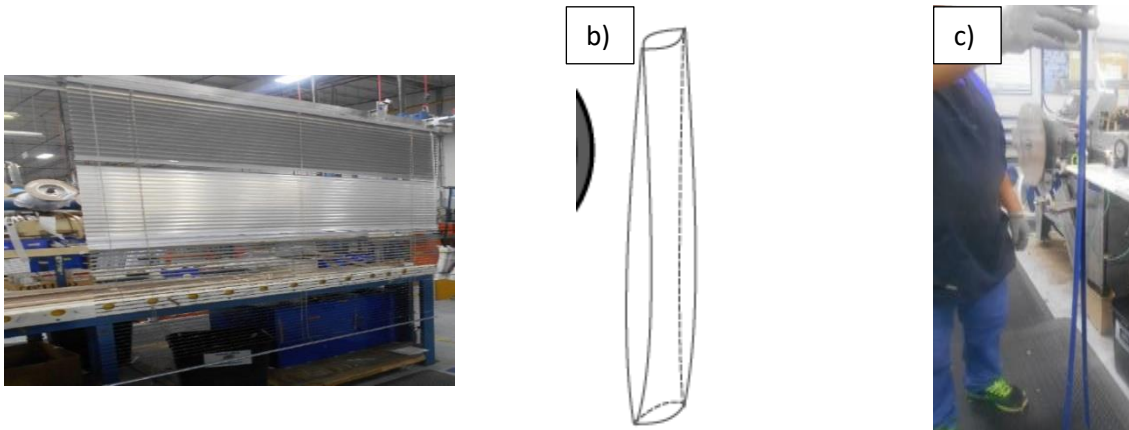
Defectos de los slats de aluminio a) Vista de defecto en persiana ensamblada b) Gap c) Arco inverso
